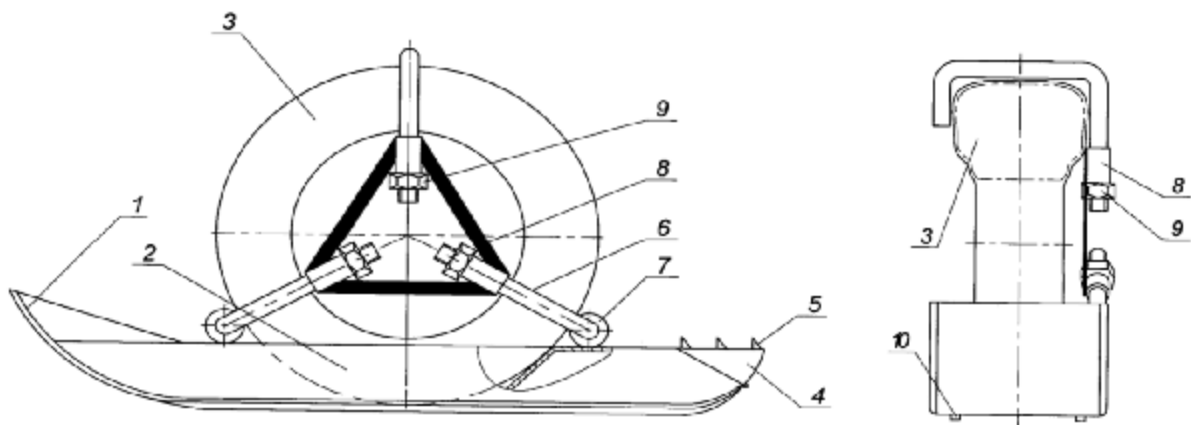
Опорная лыжа для колеса транспортного средства
